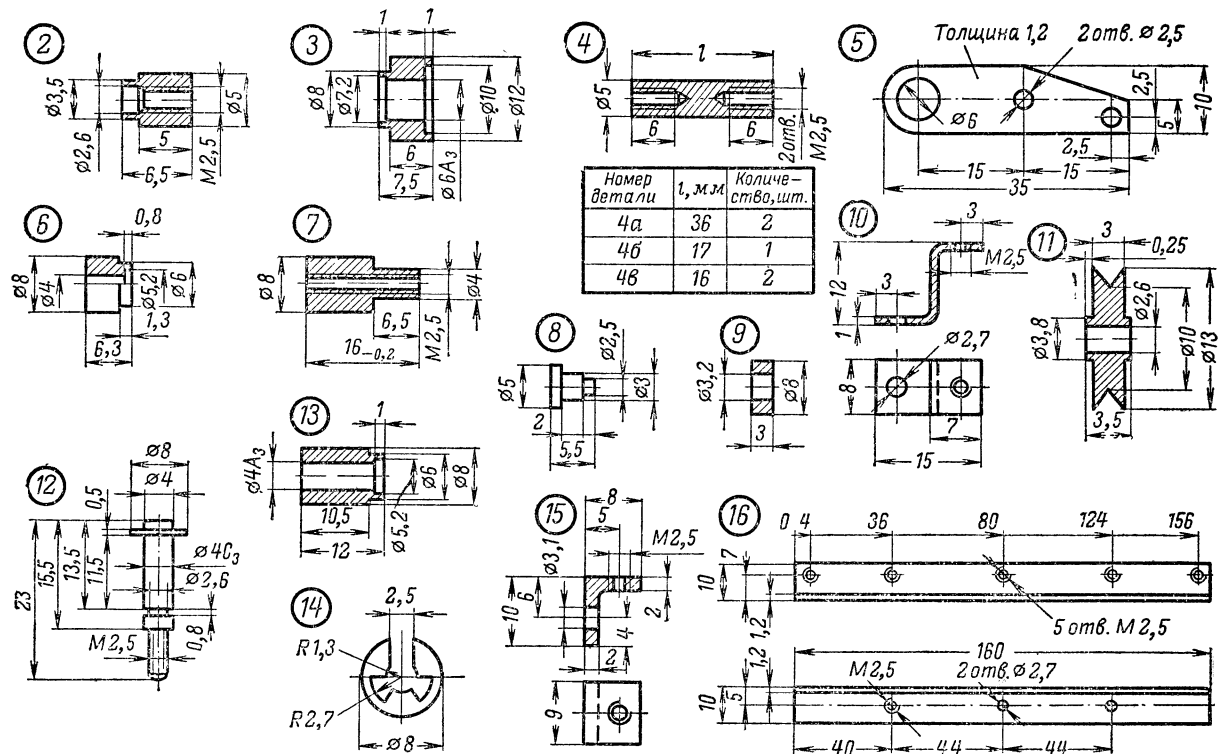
Детали лентопотяжного механизма. 2 — стойка, А12, 4 шт., развальцевать в детали 1; 3 — втулка переключателя рода работ, А12, развальцевать в детали 1; 4а, 4б, 4в — стойки, А12; 5 — рычаг фиксатора, 10кн; 6 — втулка, Л62, развальцевать в детали 5; 7 — опорная колонка, А12; 8 — ось ролика фиксатора, А12, расклепать в детали 5; 9 — ролик, 45; 10 — кронштейн, 10кн; 11 — об-
